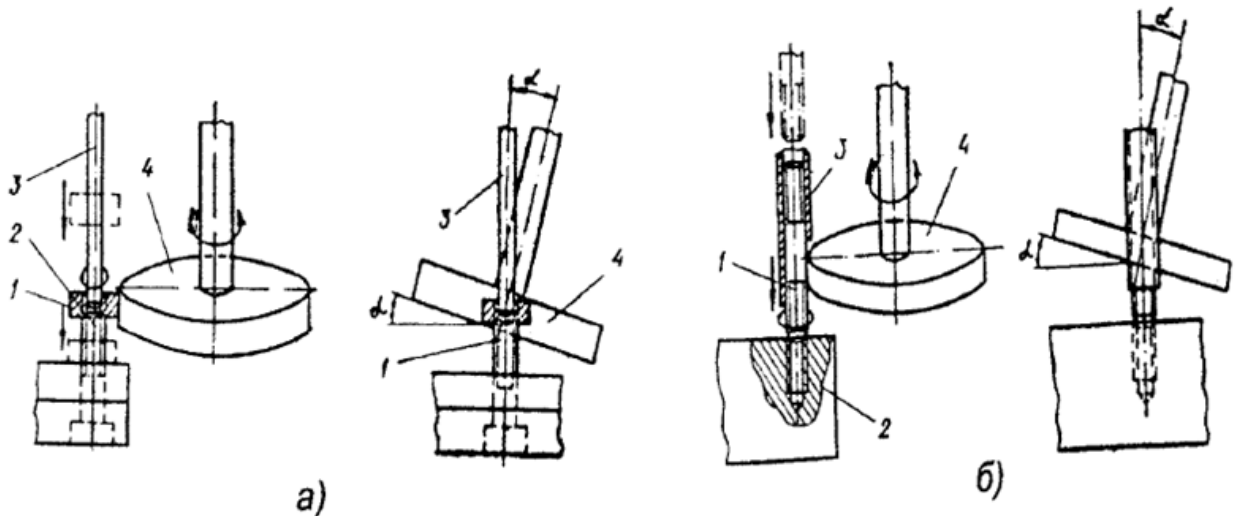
Фрикційно-інерційний спосіб загвинчування: а- гайок: 1- гайка; 2- болт; 3- напрямний стержень; б-шпильок: 1- шпилька; 2- корпус; 3- напрямна втулка.
